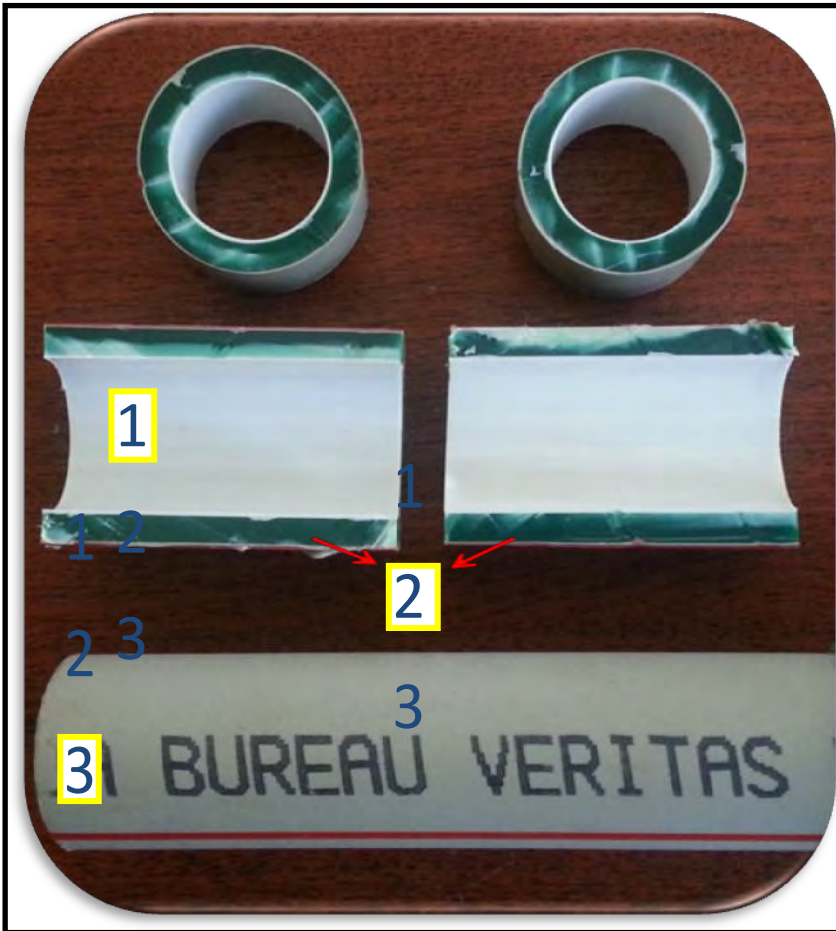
Corte transversal y longitudinal de las tuberías PP-R100
